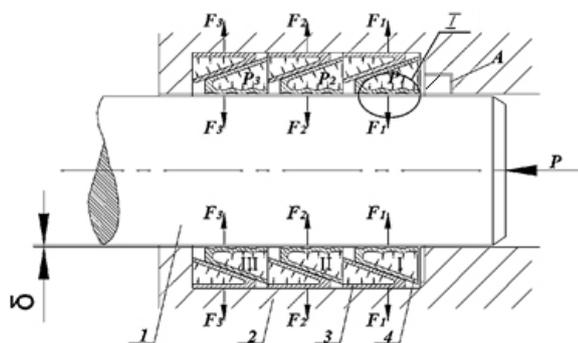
Уплотнительное устройство высоких и сверхвысоких давлений: 1 – плунжер, 2 – корпус, 3 – кольцо наружное, 4 – кольцо внутреннее.
